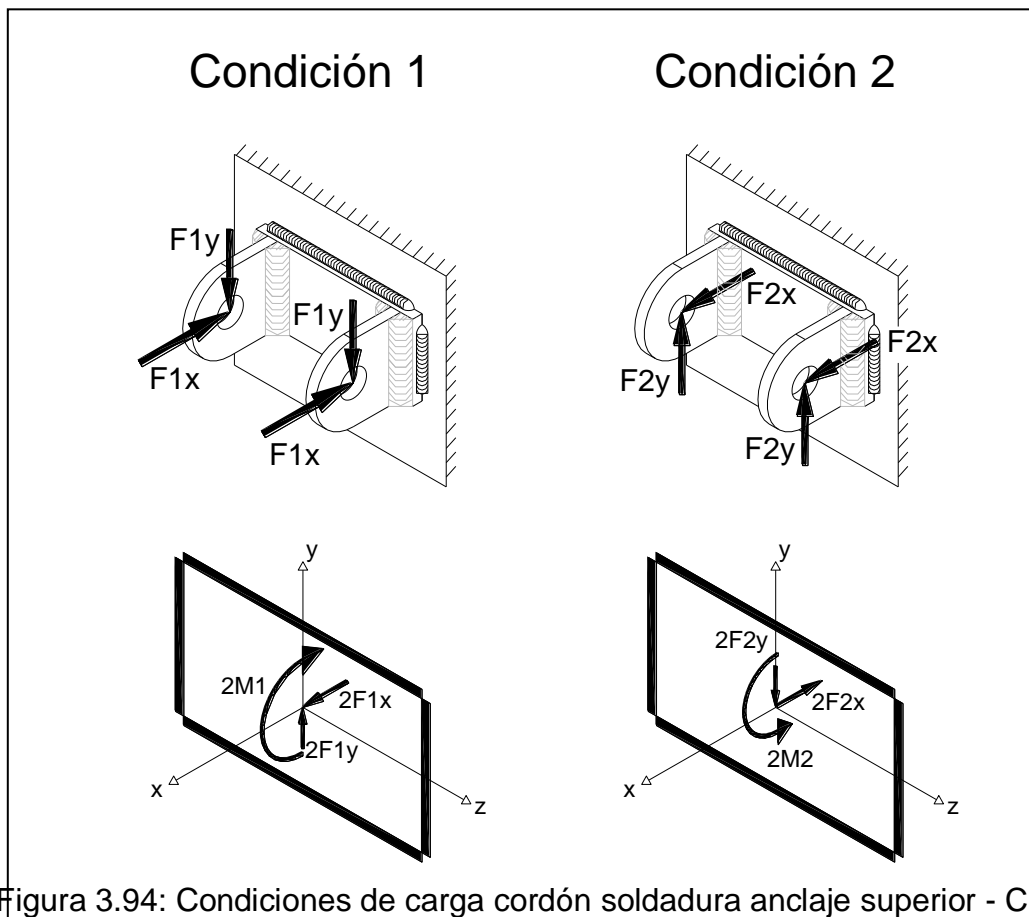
Condiciones de carga cordón soldadura anclaje superior - Chasis
